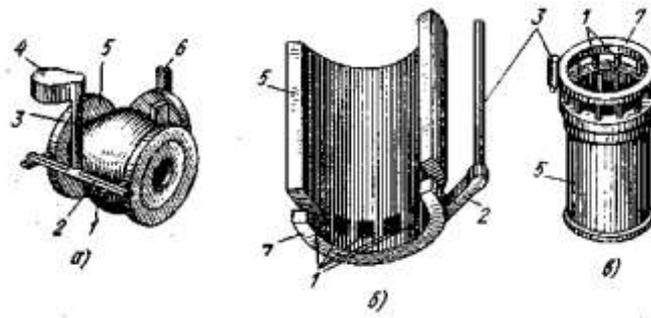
Способы подвода расплавленного металла в рабочую полость литейной формы.
